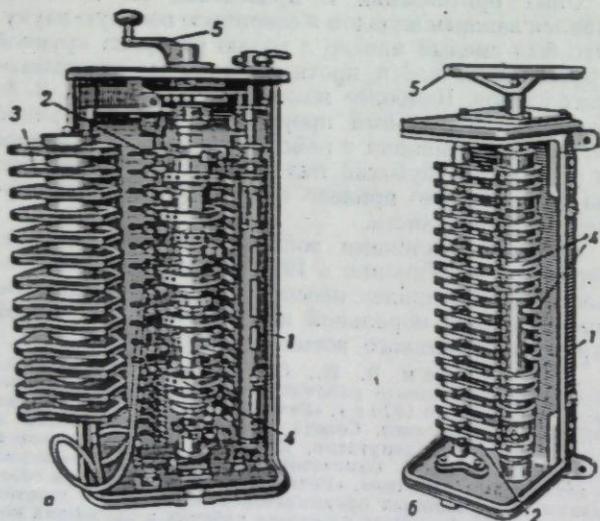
Барабанный контроллер со снятой крышней: а — трамвайного типа, б — промышленного типа; 1 — корпус; 2 — контактные пальцы; 3 — изоляционные перегородки; 4 — барабан с сегментными контактами; 5 — рукоятка.
